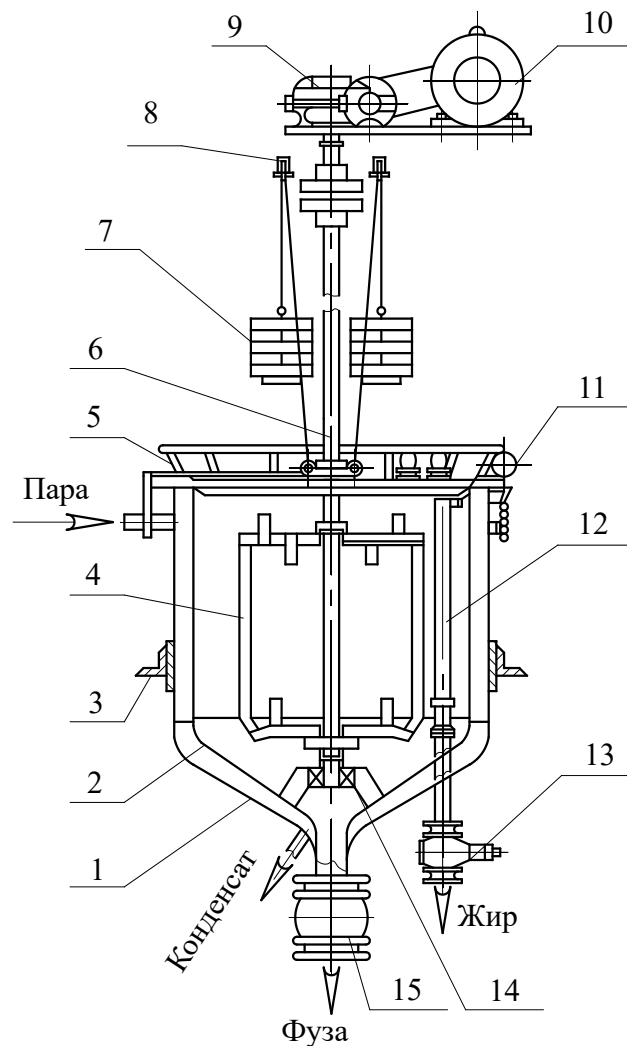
Відкритий тепловий апарат ОПК–1,25: 1 – зовнішній корпус; 2 – внутрішній корпус; 3 – опорні лапи; 4 – перемішувальний пристрій; 5 – огороження; 6 – вал; 7 – противага; 8 – блок; 9 – черв'ячний редуктор; 10 – електродвигун; 11 – манометр; 12 – поворотна труба, 13 – вентиль для зливання жиру; 14 – радіально-упорний підшипник; 15 – вентиль для зливання фузи
